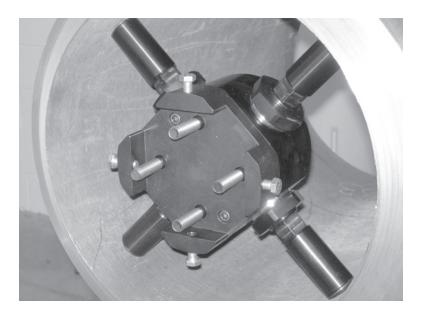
Снимите центровочный указатель, гайки и шайбы со шпилек зажимного патрона.
